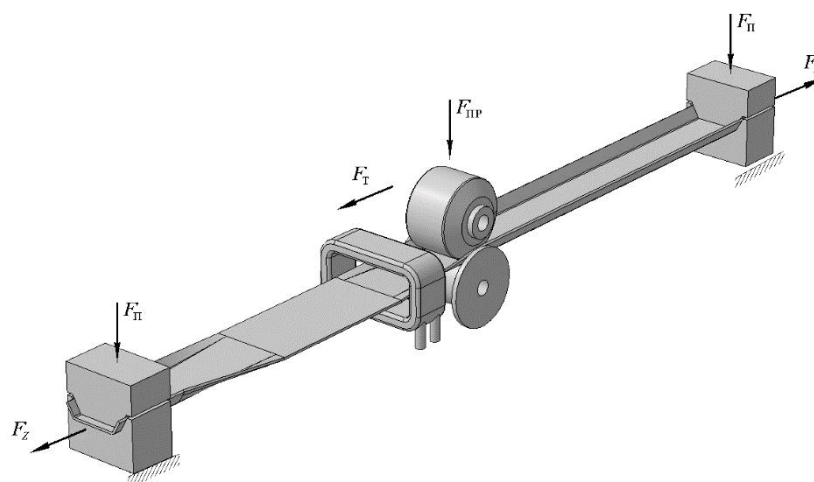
Способ изготовления профилей с нагревом заготовки токами высокой частоты
